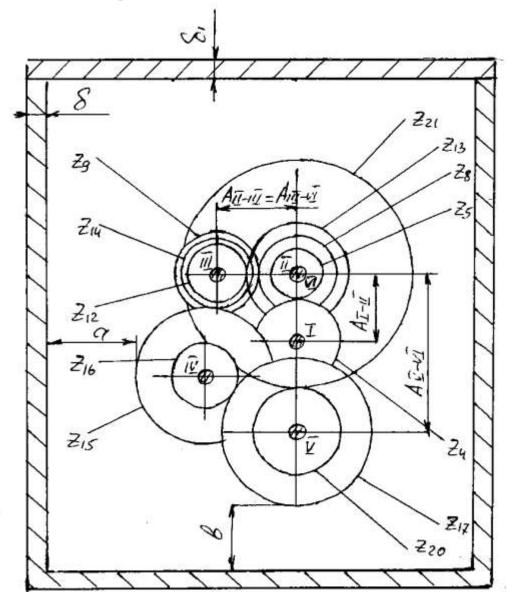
Эскизная компоновка свертки коробки скоростей.
